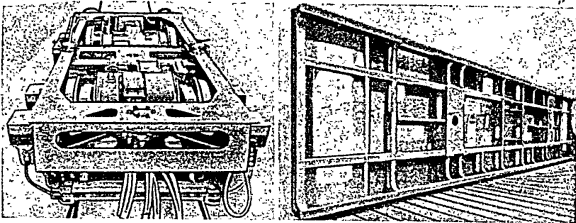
Geschweißtes Drehgestell der E44 mit fertig eingebauten Fahrmotoren
